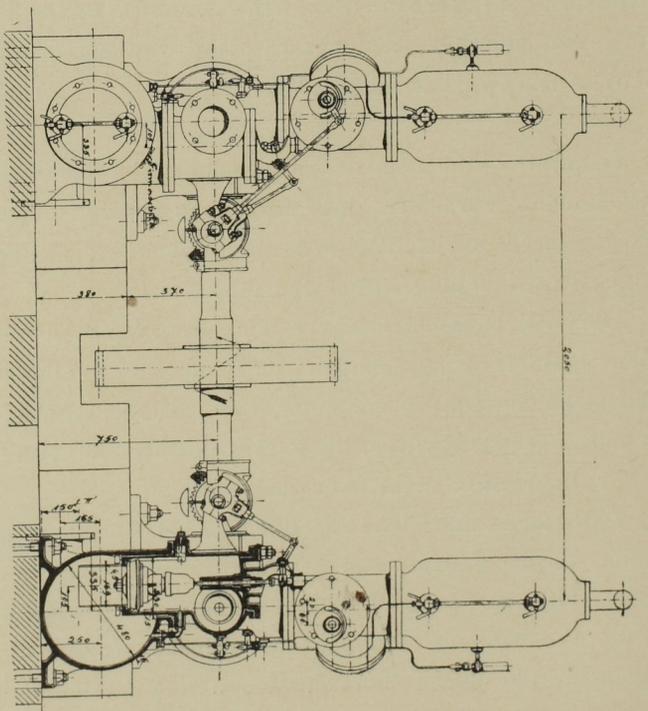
Stirnansicht und Querschnitt der Pumpe.
